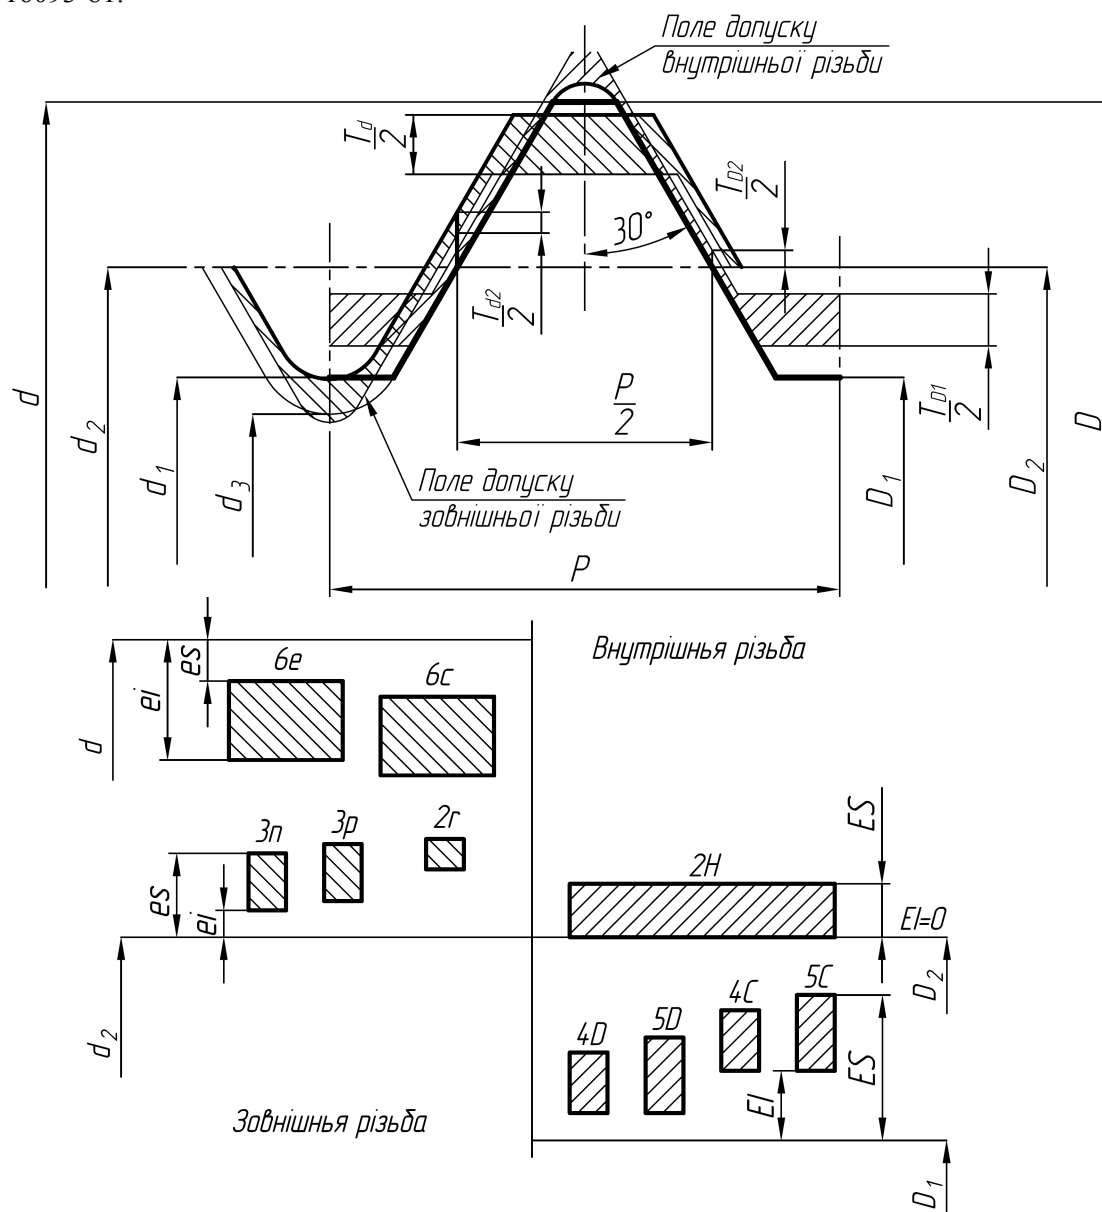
Поля допусків різьбового з'єднання з натягом
